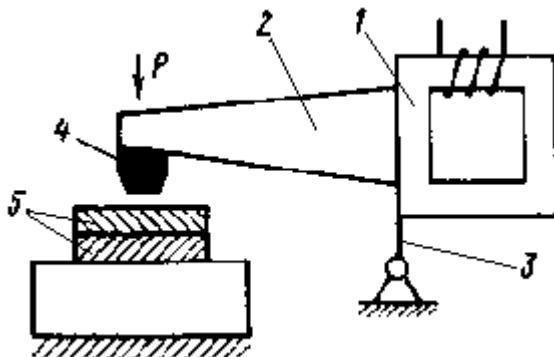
Схема ультразвуковой сварки:
